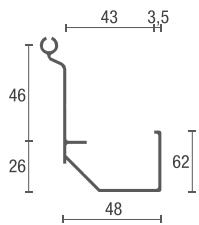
DETAIL SPOJOVACÍHO ALU PROFILU
